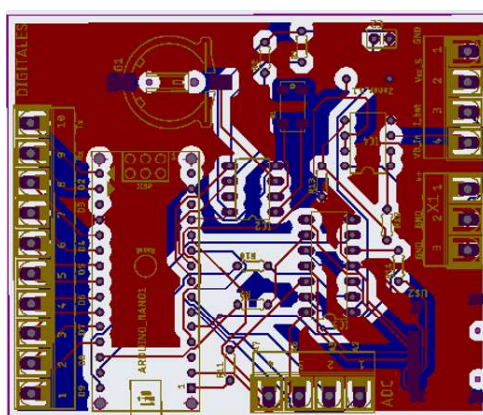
Circuito carga PCB tarjeta de adquisición de datos
